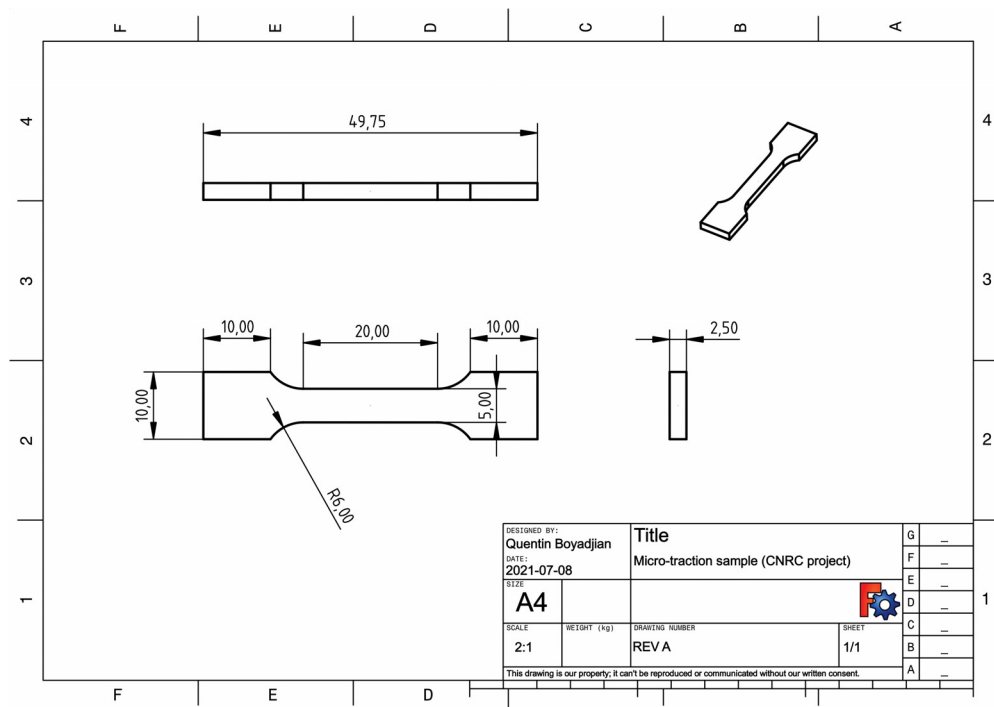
Plan d'usinage des éprouvettes de traction.
